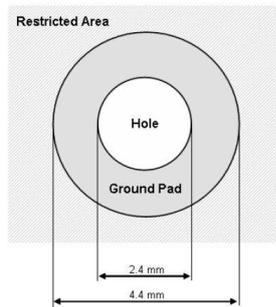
Dimensiones físicas de los orificios de soporte del módulo.
